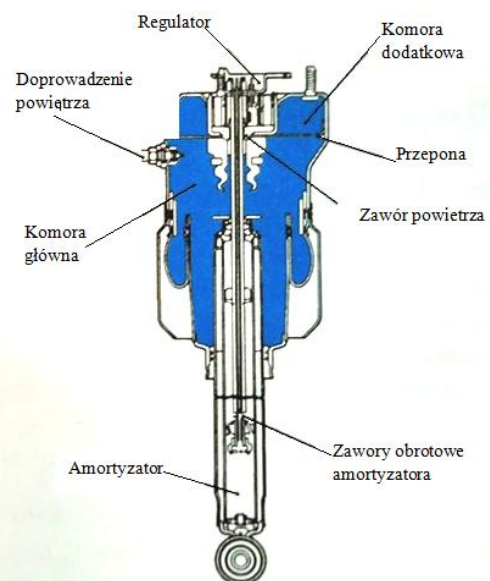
Schemat działania gumowego miecha w zawieszeniu pneumatycznym [12]
